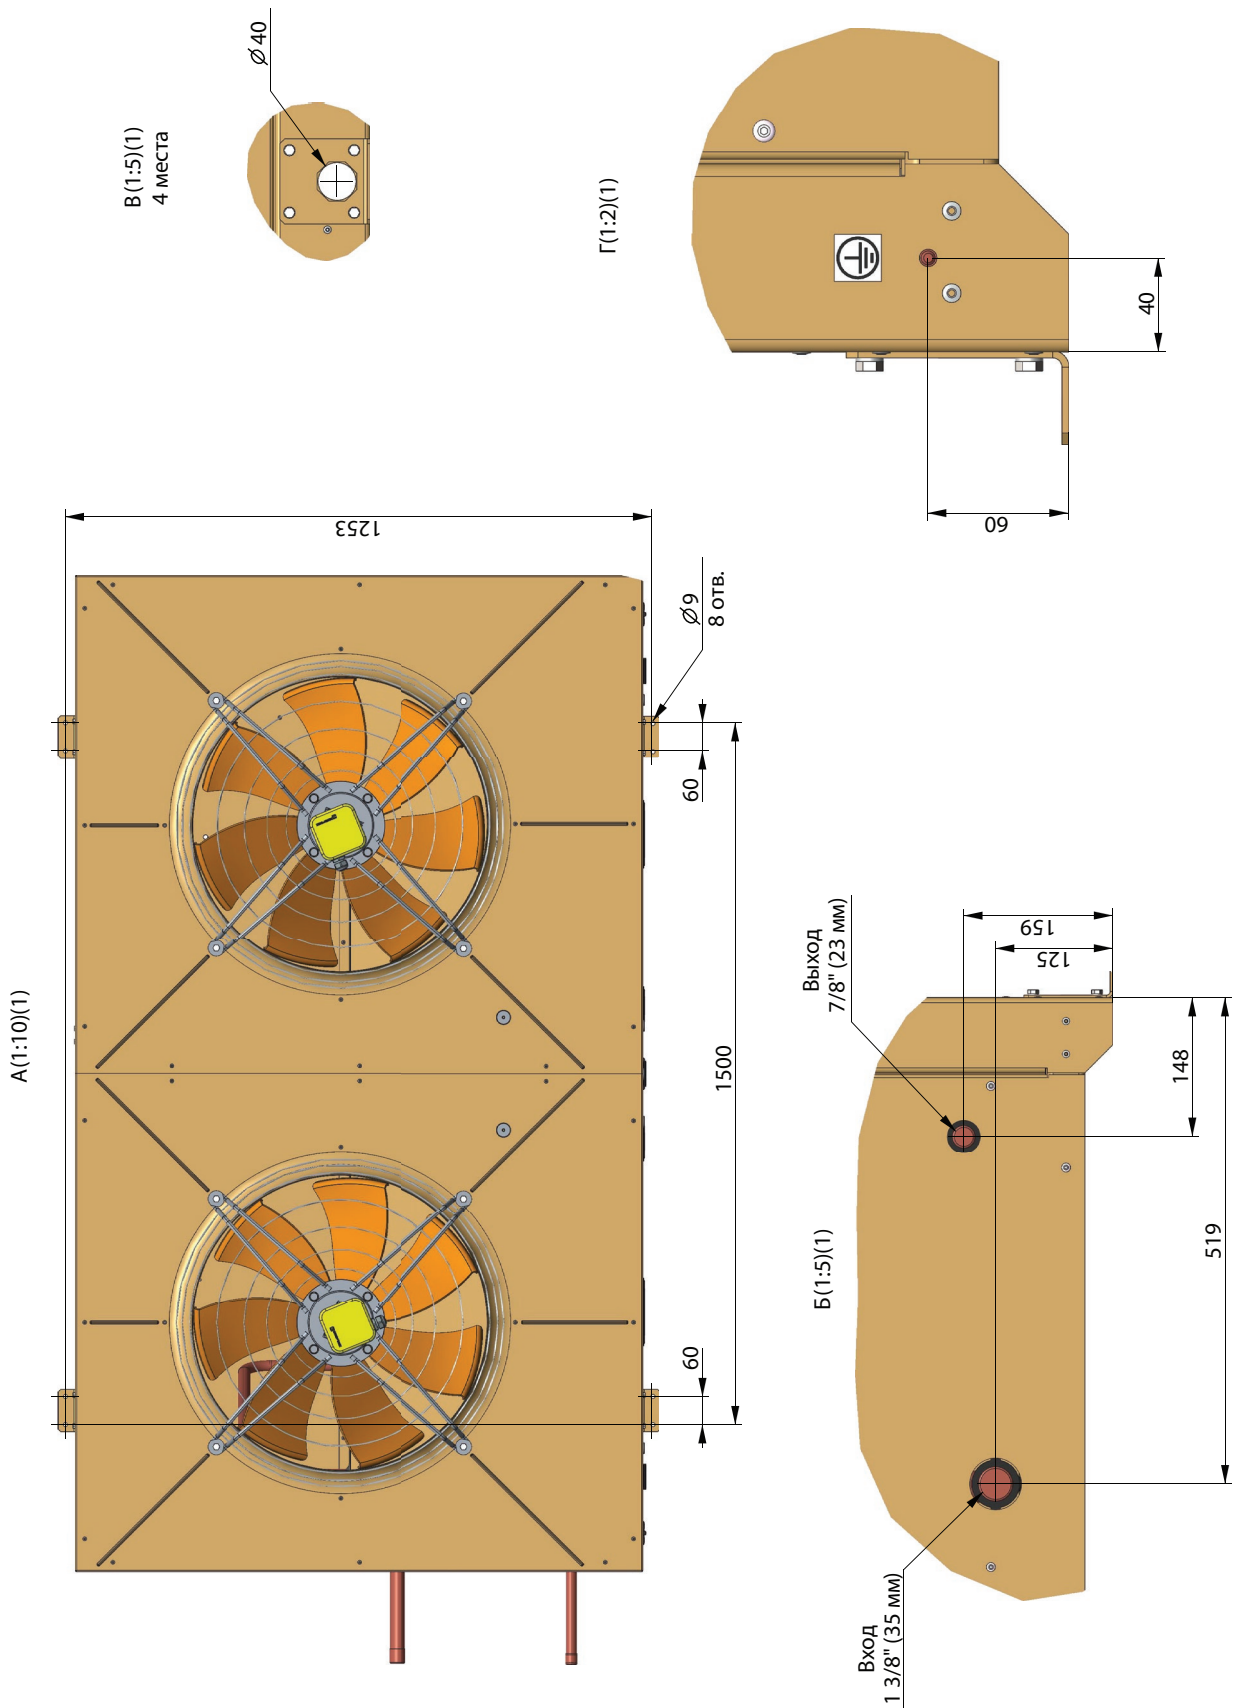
Агрегат компрессорный типа МАКК 320-551, -651, -701
